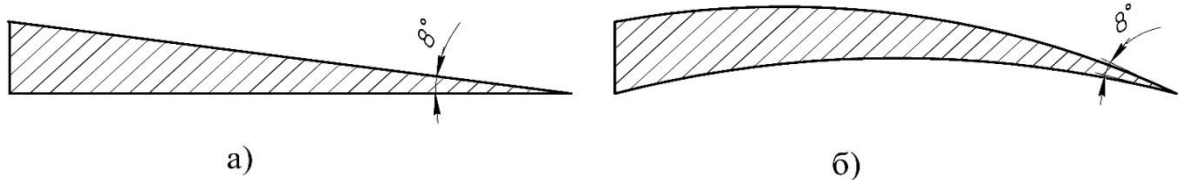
Профили сечений лопасти СКВ: а – с прямой поверхностью; б – с искривленной поверхностью
